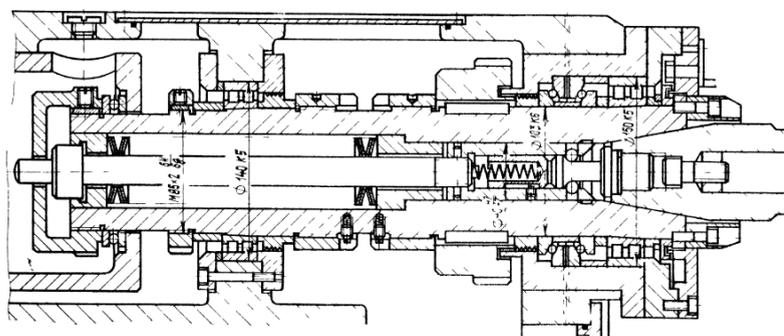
Пример чертежа конструкций шпиндельного узла
